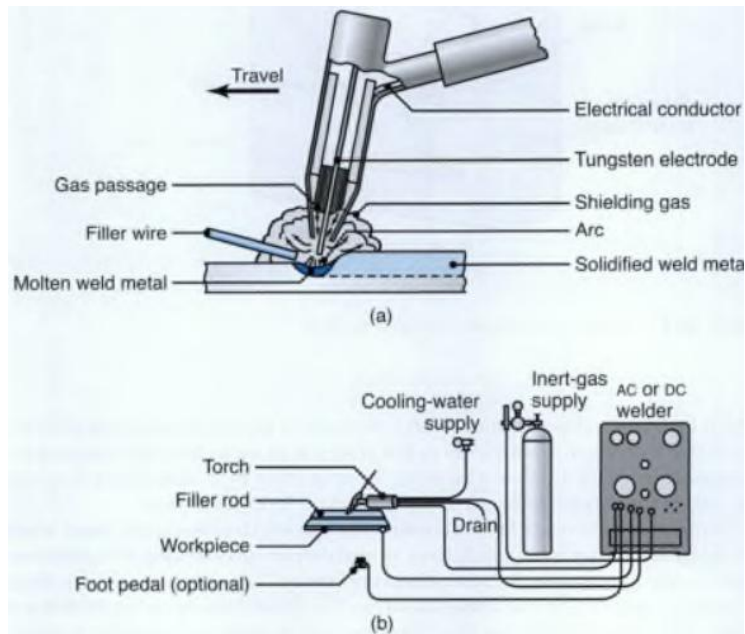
A) SOLDADURA TIG (TUNGSTEN INERT GAS), B) EQUIPO UTILIZADO PARA SOLDADURA TIG [70].
